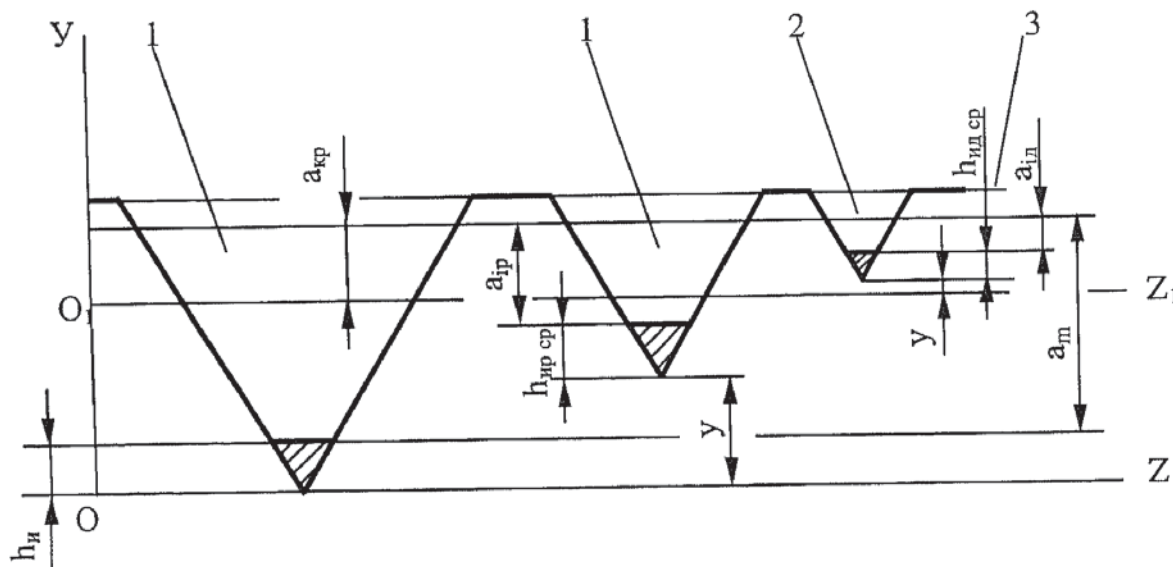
Схема расположения абразивных зерен круга: 1 — режущие зерна; 2 — пластически деформирующее зерно; 3 — условная поверхность связки круга
